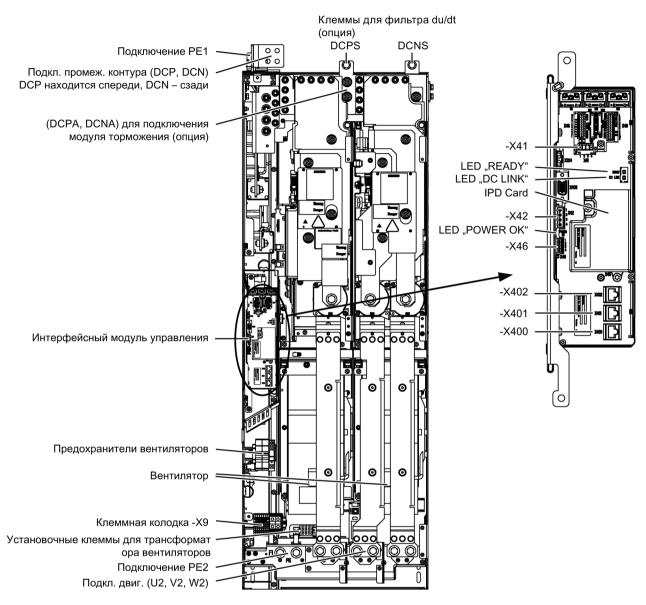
Модуль двигателя, типоразмер НХ
